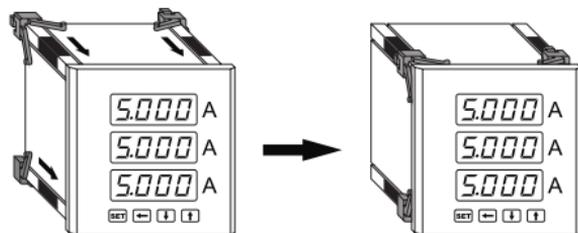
Схема крепления фиксаторов на корпус /
